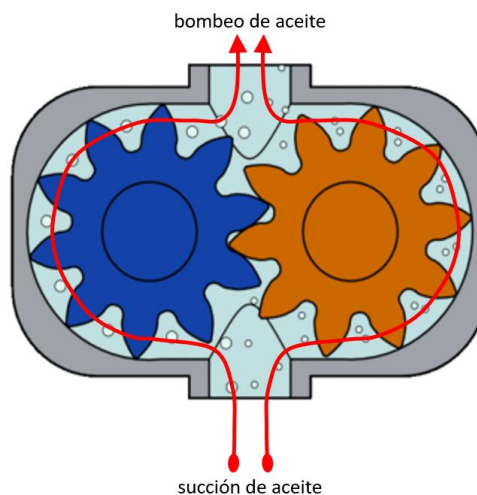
Vista de sección del cuerpo de una bomba hidráulica de engranajes (fuente: Internet)
